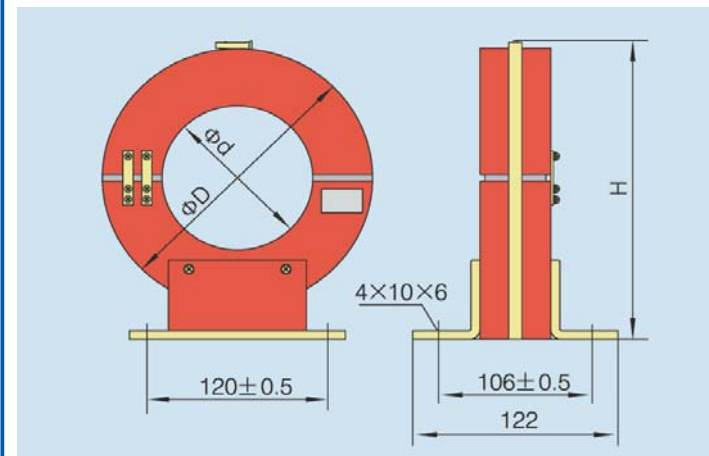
Внешний вид и размеры трансформатор тока нулевой последовательности LХК-80(100,120)
